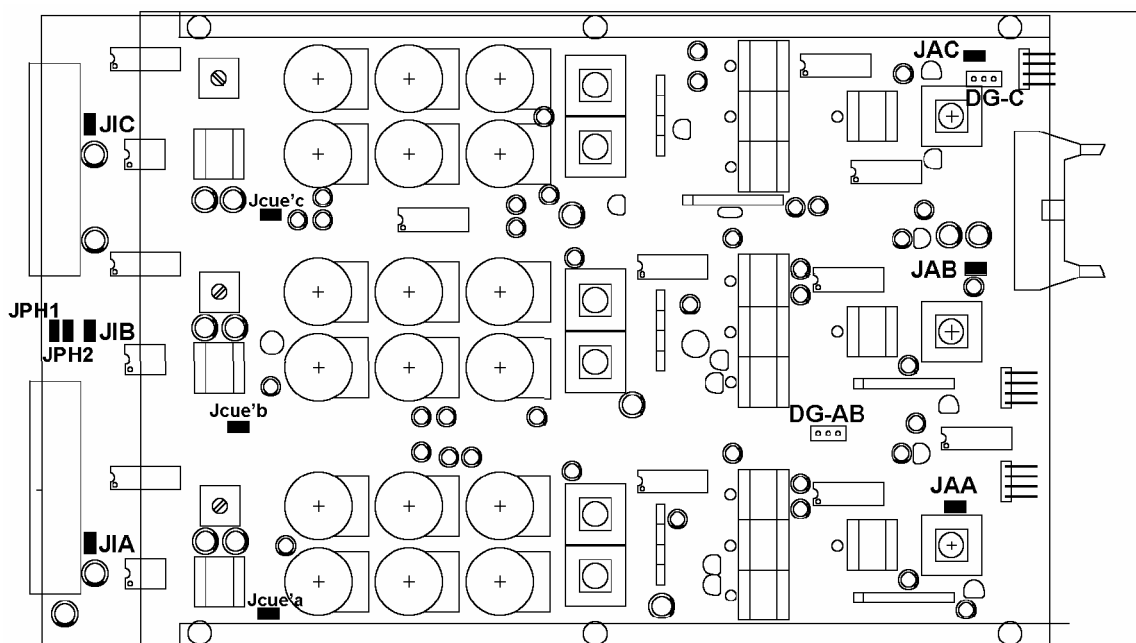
Módulo de micrófono 2312 (vista lado soldaduras)
